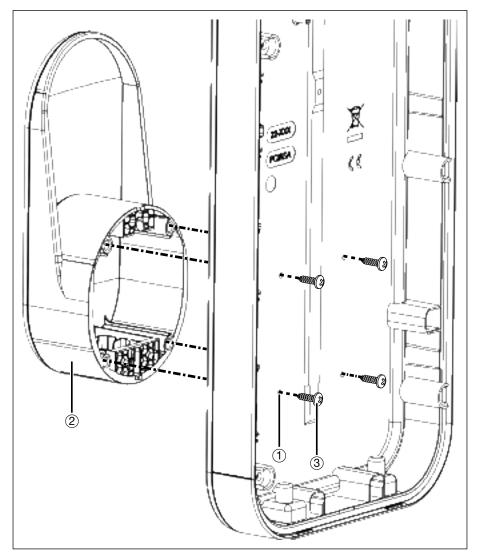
Montagem do suporte para cabos ao posto de carregamento
